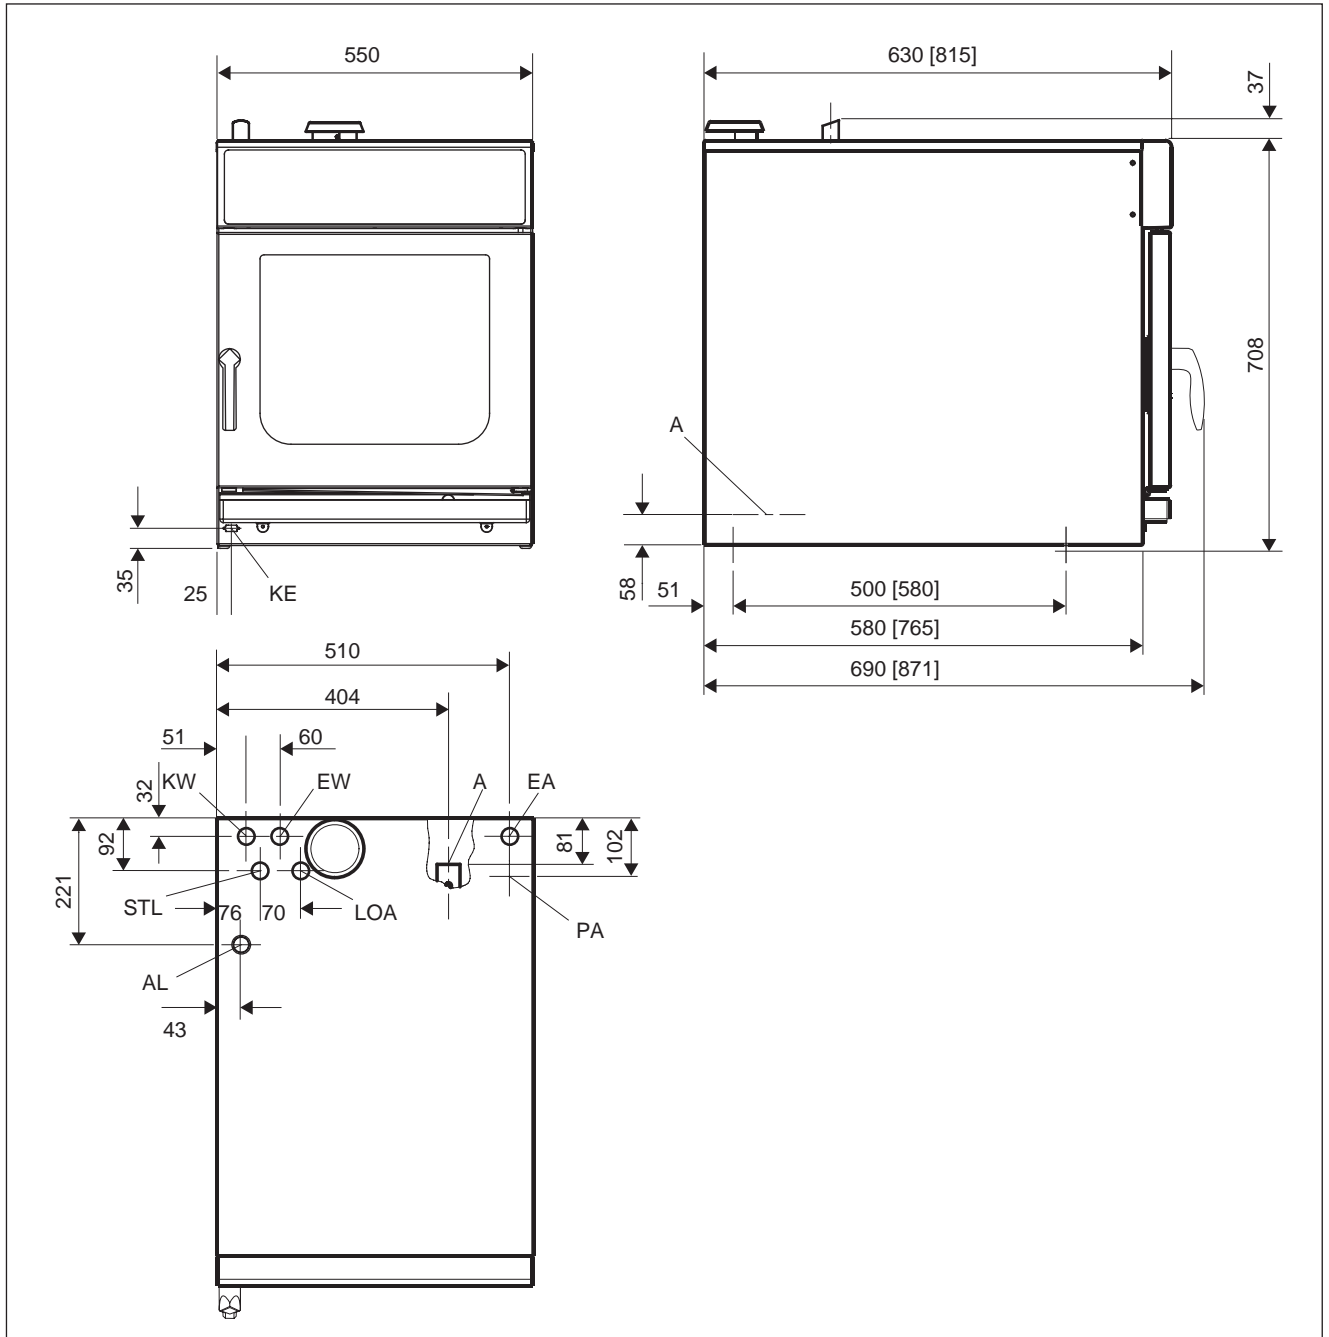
Combi-cuiseurs 605/610, dimensions en mm
